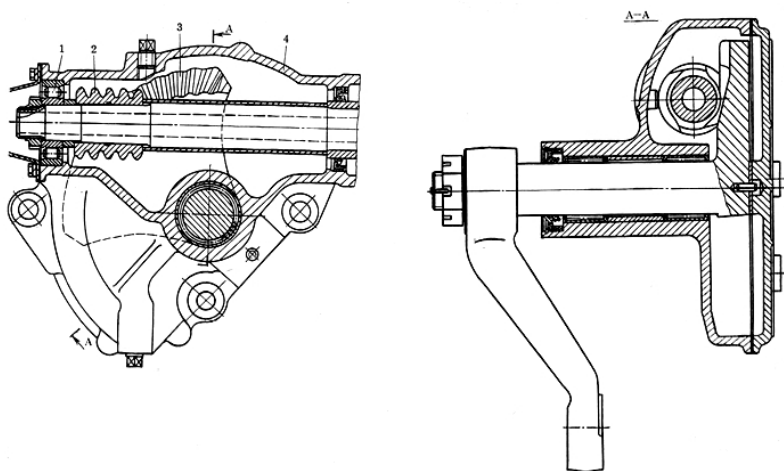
Рулевой механизм типа цилиндрический червяк — боковой сектор
